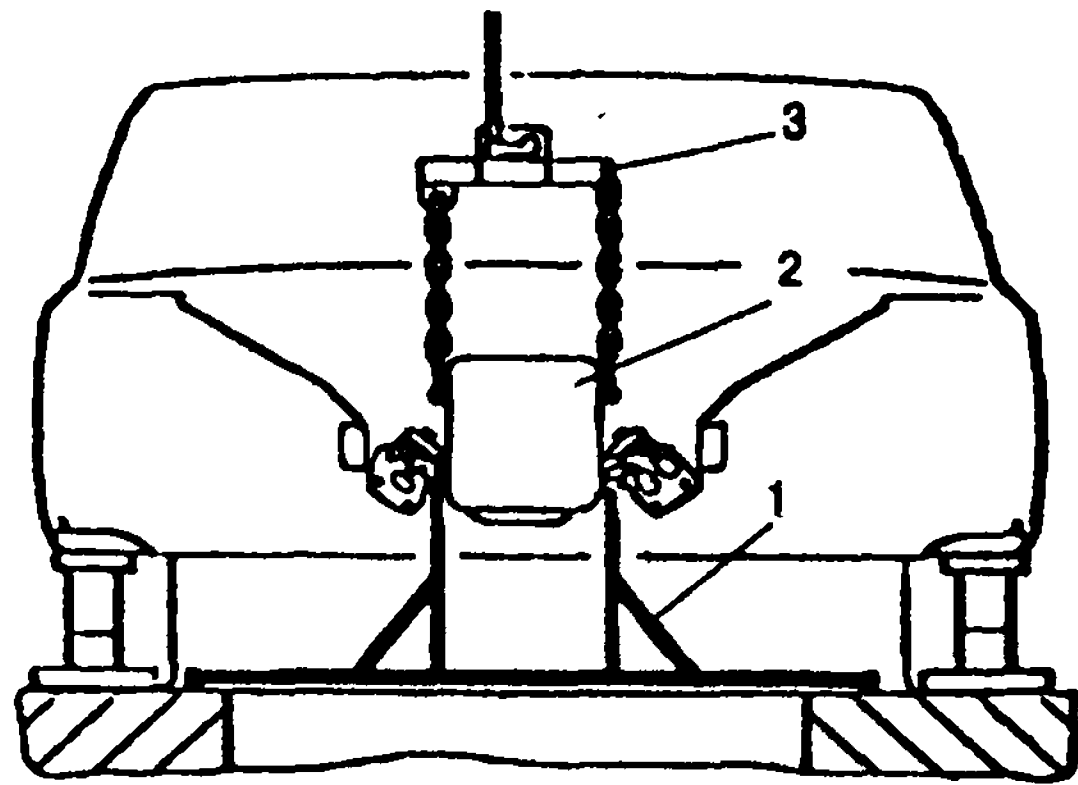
Установка подставки под двигатель: 1 - подставка; 2 - двигатель; 3 - захват
